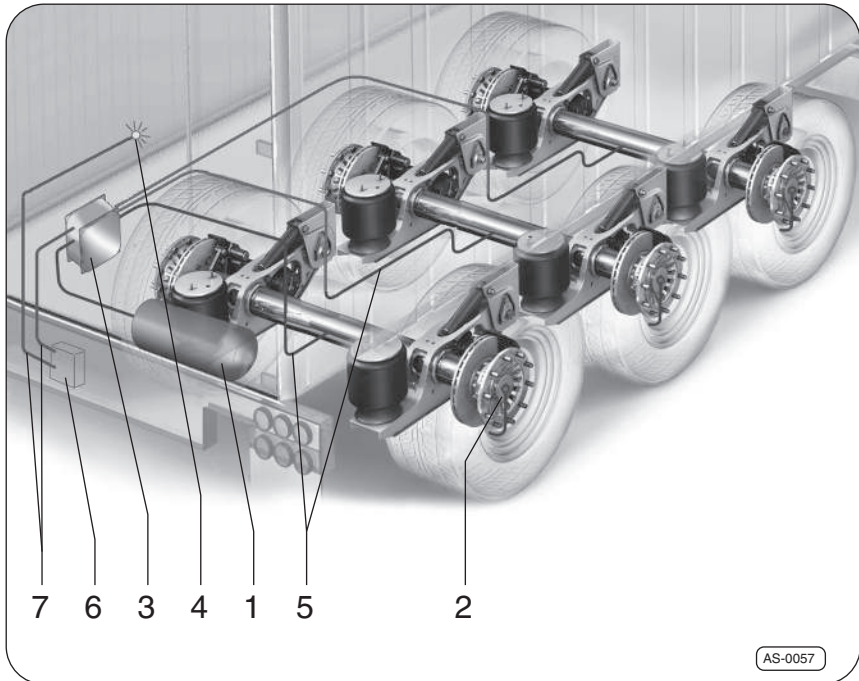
· Montage d'ensemble de SAF TIRE PILOT
